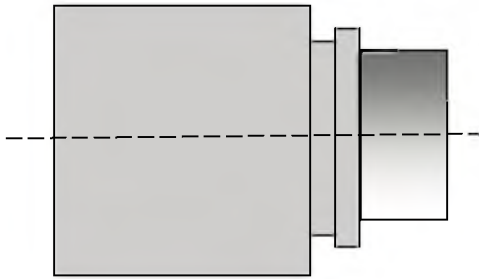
Поршень суппорта тормозного механизма типа «TEVES» с пьезоактуатором, который расположен внутри поршня
